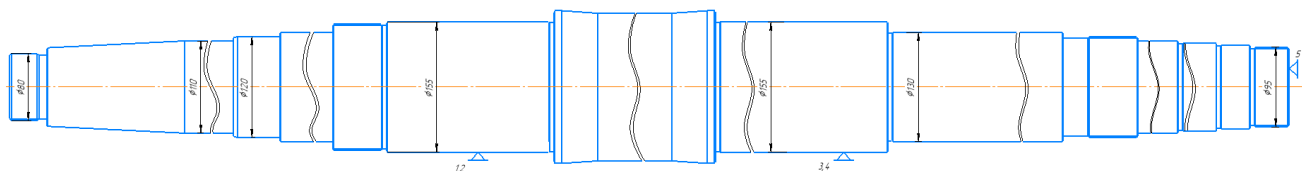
Схема базування деталі Вал Н12.178.34.01 у виробі.
